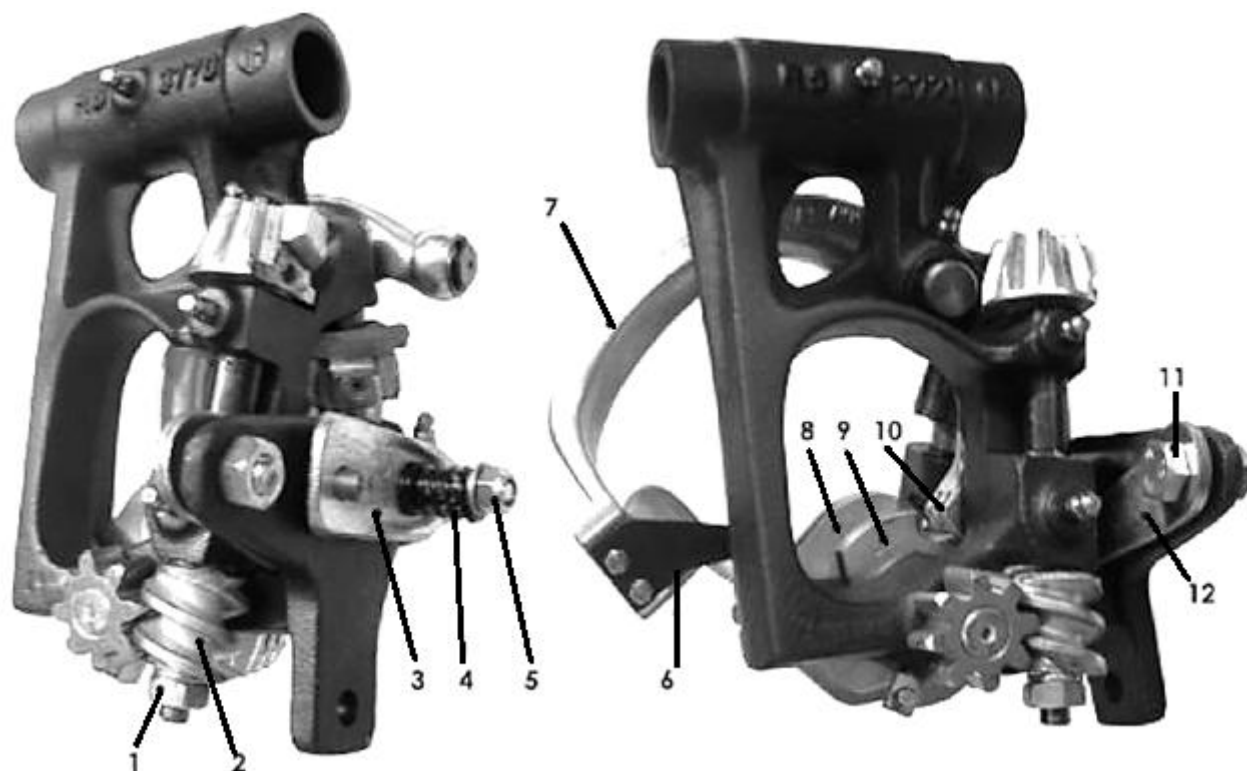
Узловязатель: 1 – гайка; 2 – червяк; 3 – замыкатель; 4 – пружина; 5 – гайка; 6 – нож; 7 – ножевой рычаг; 8 – очиститель; 9 – двойной диск; 10 – держатель шпагата; 11 – болт; 12 – рычаг
